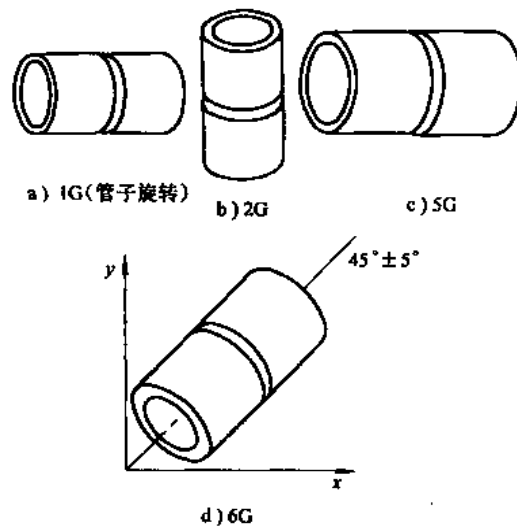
开坡口对接焊缝管试件的焊接位置
